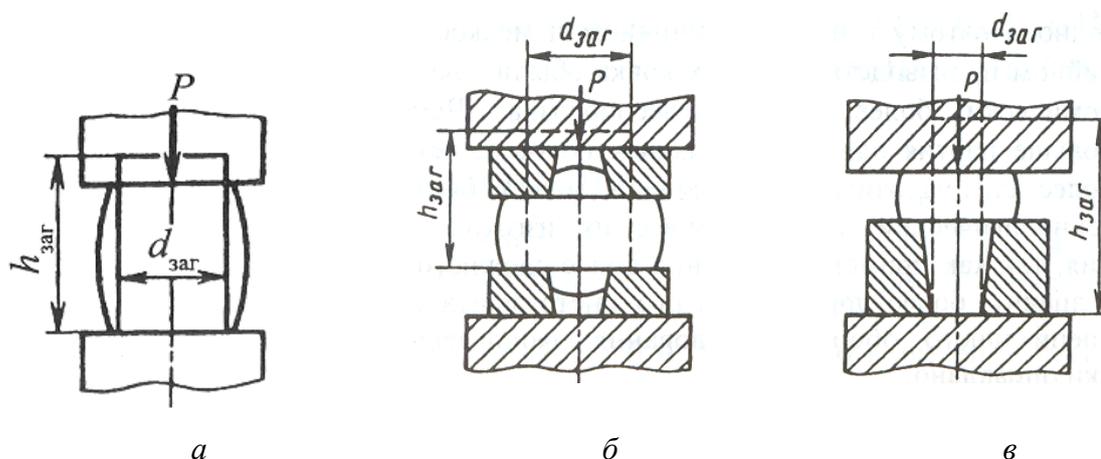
Схемы осадки: *а* — между плоскопараллельными бойками;
